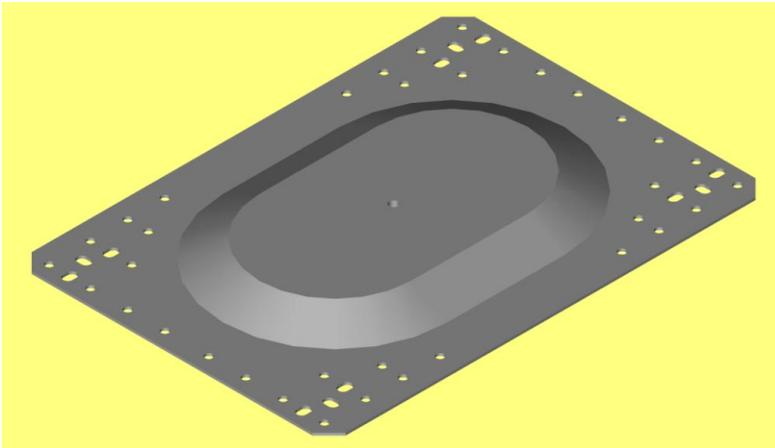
Grundplatte zur Montage auf Betondächern
